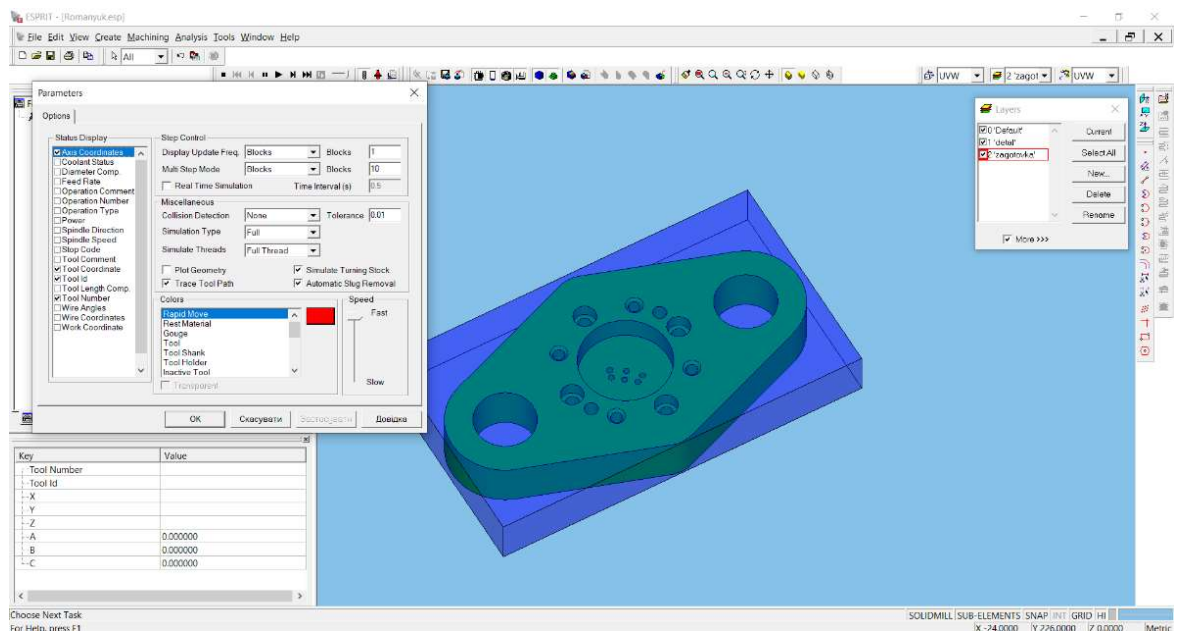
Створення заготовки деталі кришка у САМ Esprit
